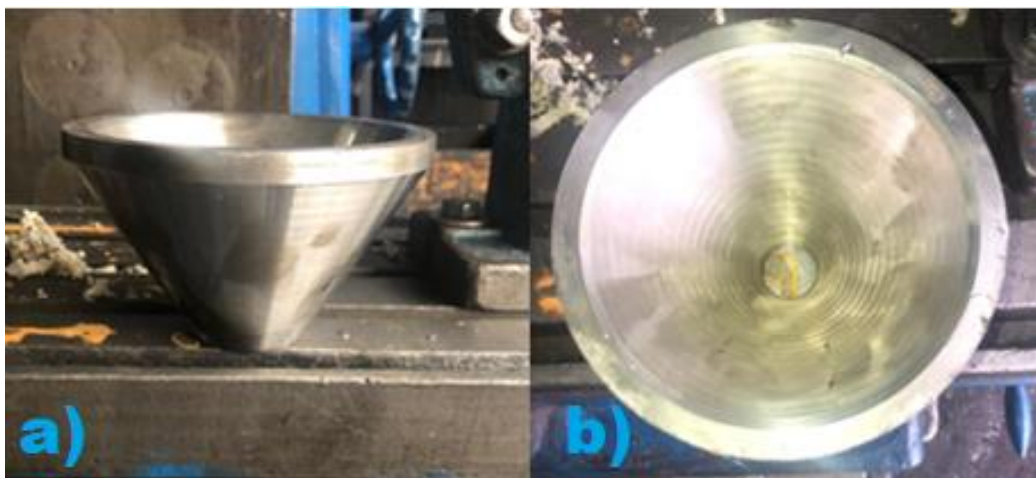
Elemento final: Tobera. a) Vista isométrica. b) Vista superior.
